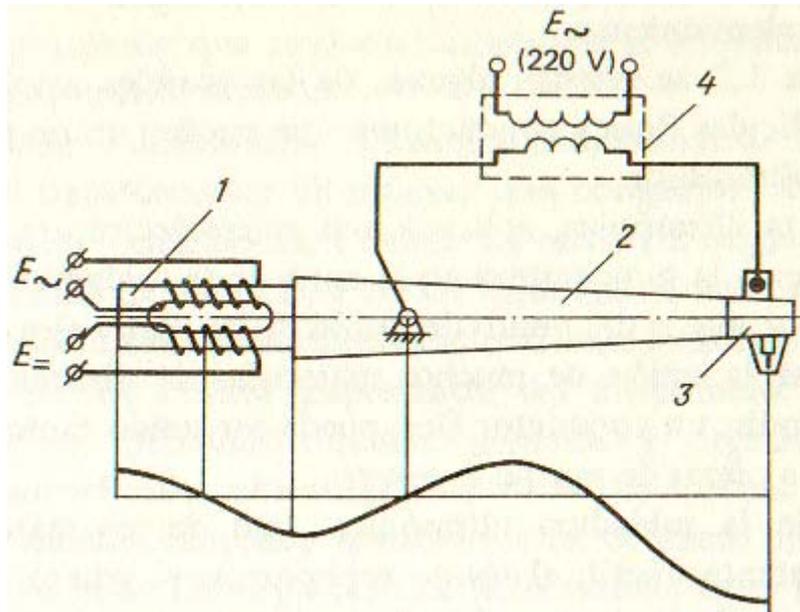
Soldadura Ultrasónica con Caldeo Indirecto por Impulsos: 1- transformador magnetoestrictivo; 2- guía ondas; 3- instrumento soldador; 4- fuente de alimentación para el caldeo del instrumento soldador.
